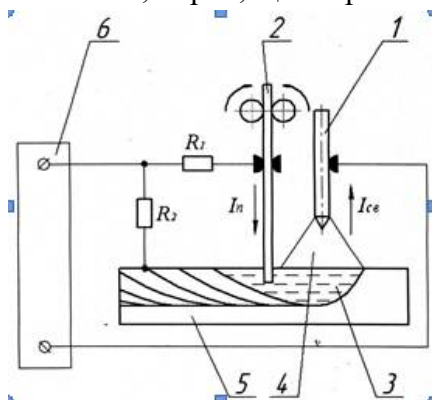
Схема процесу зварювання: 1 – електродний дріт; 2 – присадковий дріт; 3 – зварна ванна; 4 – зварна дуга; 5 – виріб; 6 – джерело живлення
